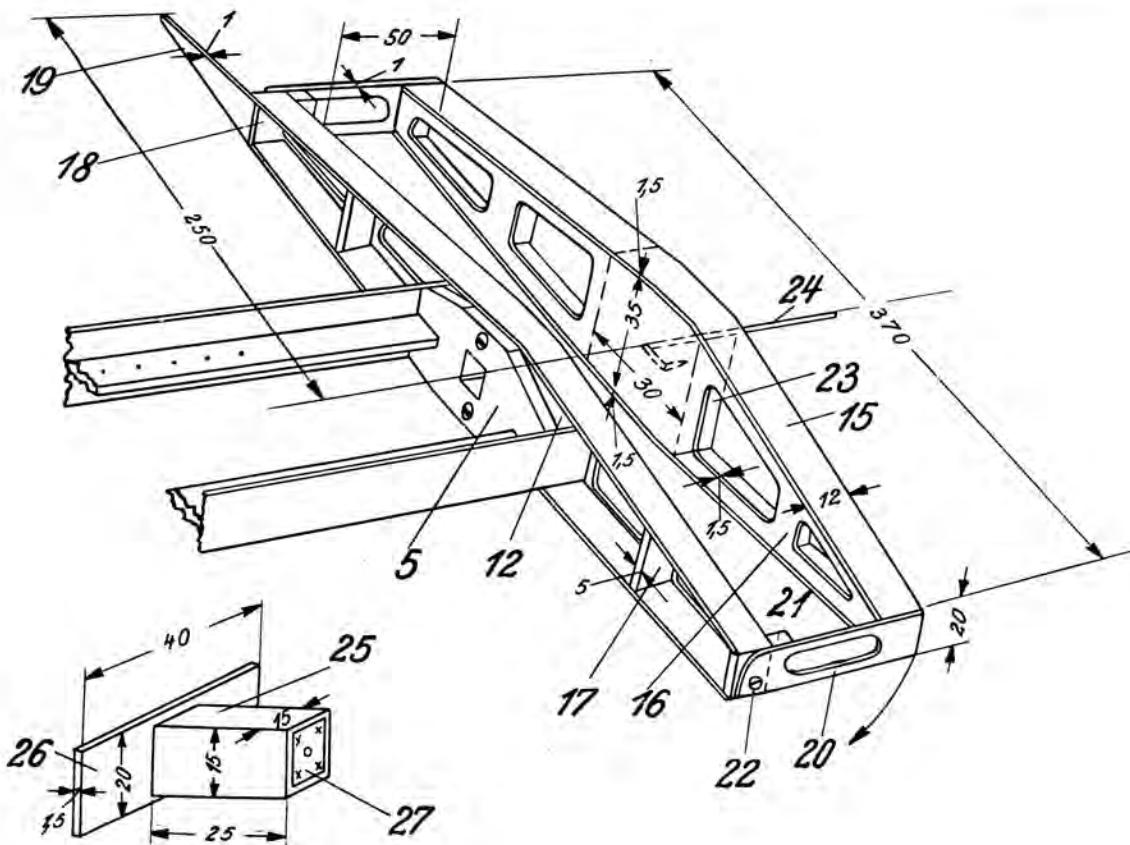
Der Querrahmen und das Luftschraubenlager.
